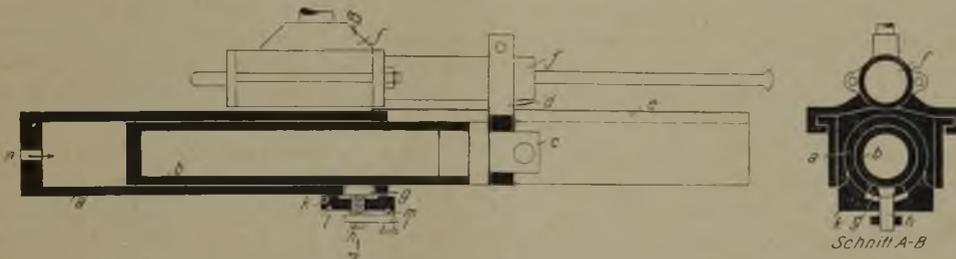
Vorschubregelung der Bohrmaschinenfabrik Glückauf.
